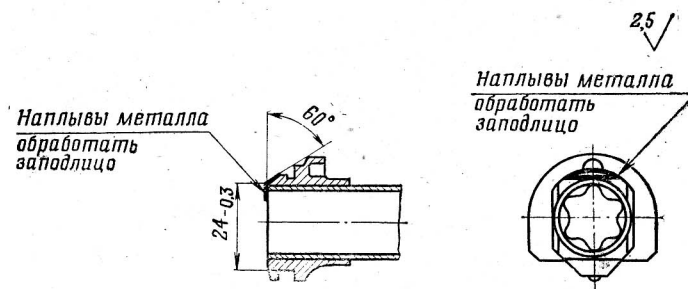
Обработка скоса на основании ствольной накладки после наплавки
